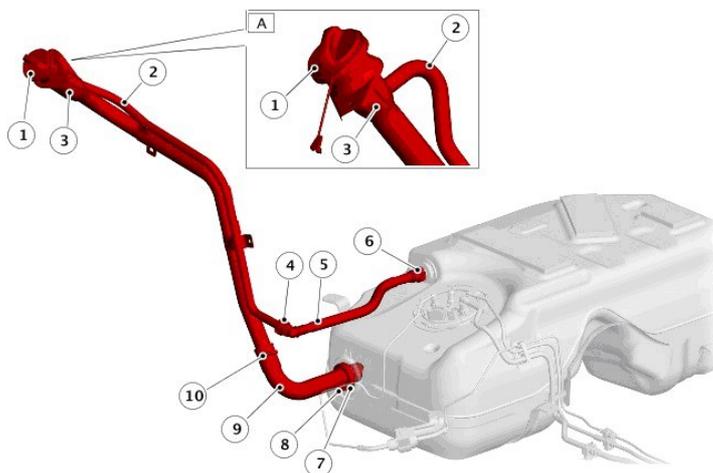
Заливной патрубок топливного бака в сборе с сапуном
